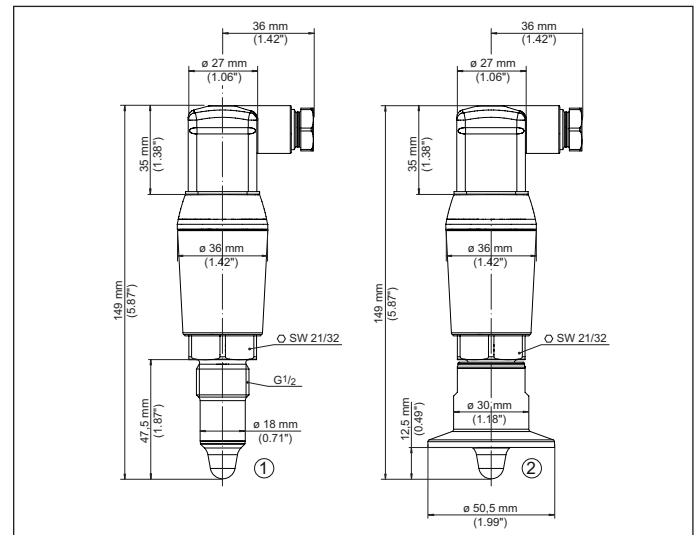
VEGAPOINT 31, Hygieneausführung - Gewinde mit ISO 4400-Stecker
